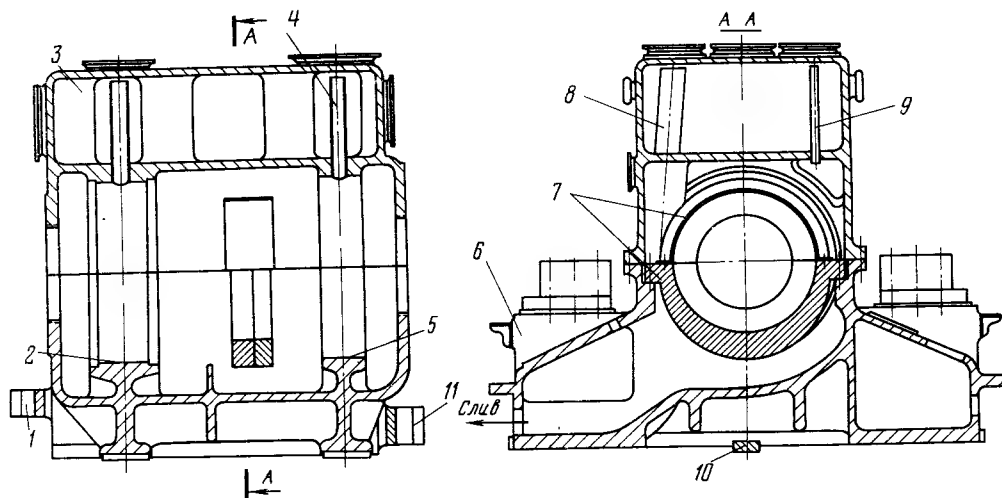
Литой корпус среднего подшипника турбины К-800-240 ЛМЗ:
